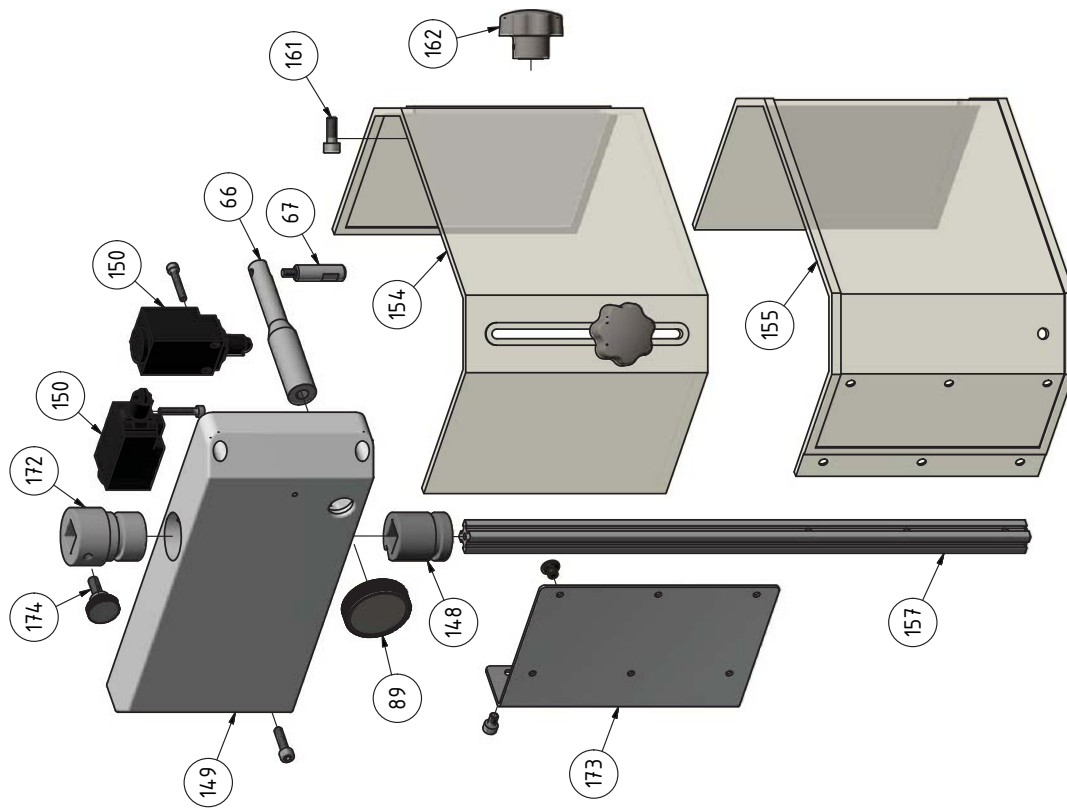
Fräsfutterschutz - Mill chuck safety
